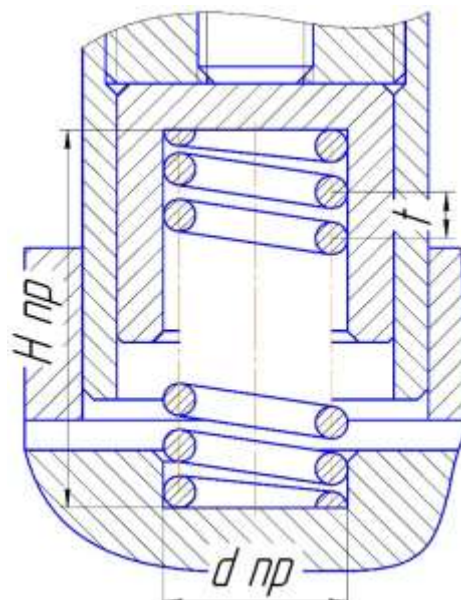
Камера под установку пружины на крышке валковой подачи
